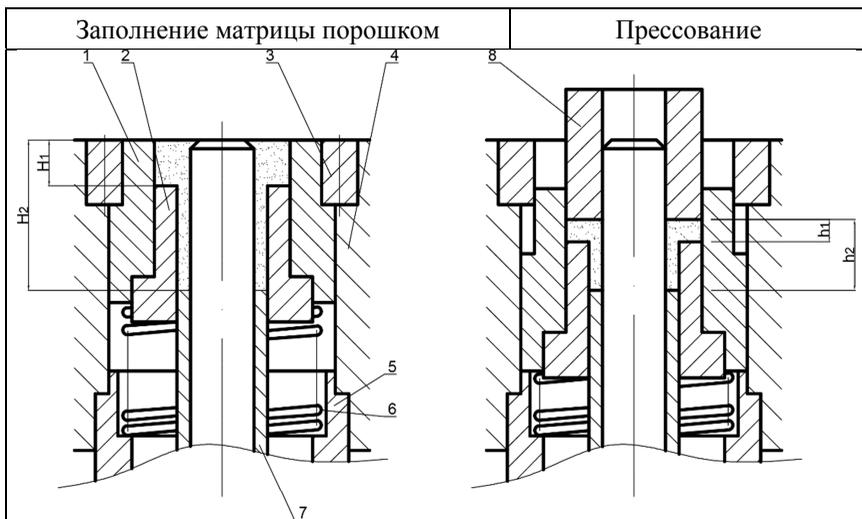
Схема пресс-формы для прессования втулок с наружным верхним буртом:
